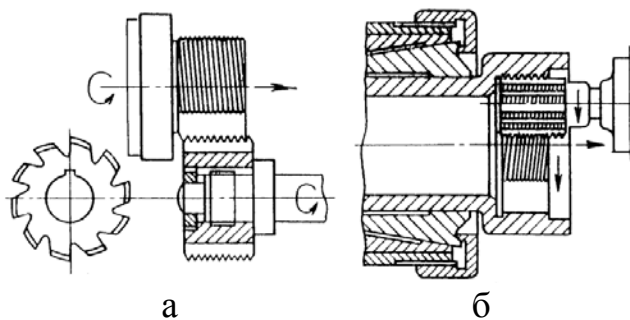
Схема нарізування різьби гребінчастою фрезою: а – зовнішньої; б – внутрішньої.
